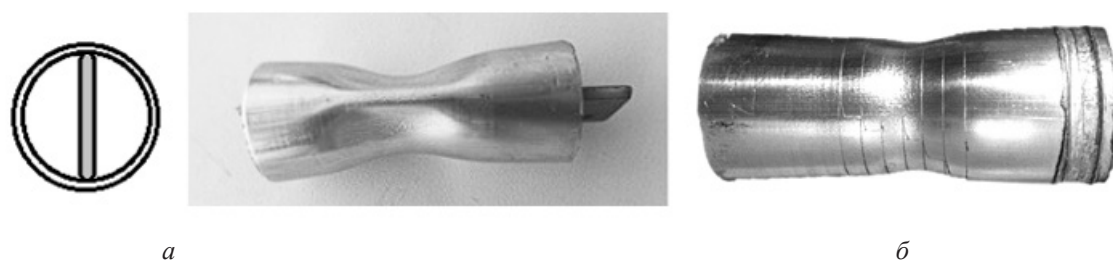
Расположение распорки в заготовке (а); макет изделия (б)
